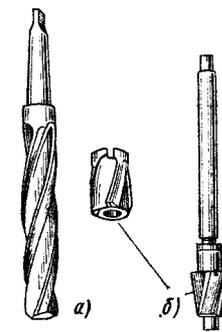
Зенкеры: а — цилиндрический; б — конический
